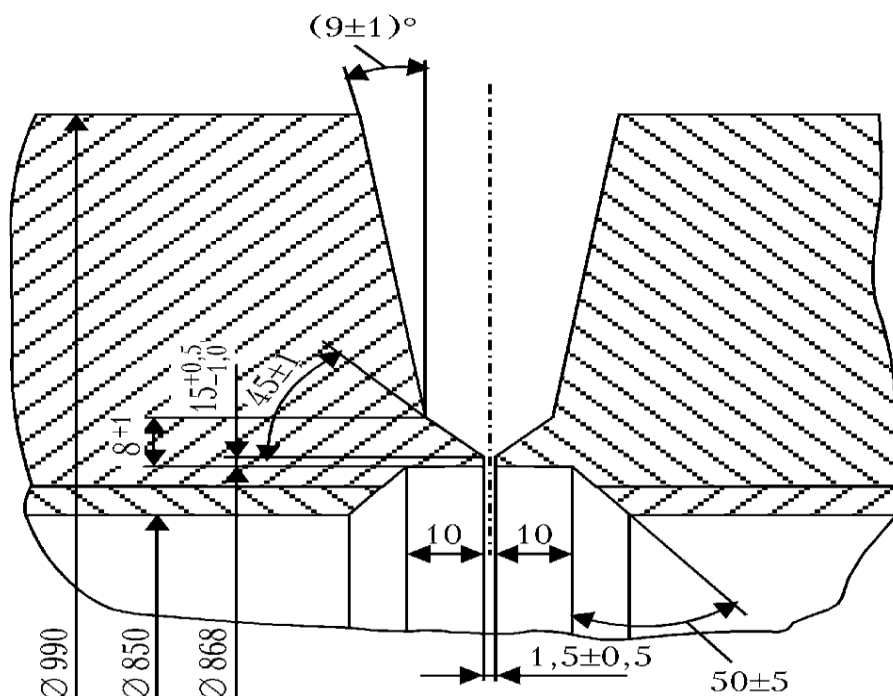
Схема стандартной разделки кромок сварных соединений, полученных способом ААрДС неплавящимся электродом с применением сварочной проволоки
